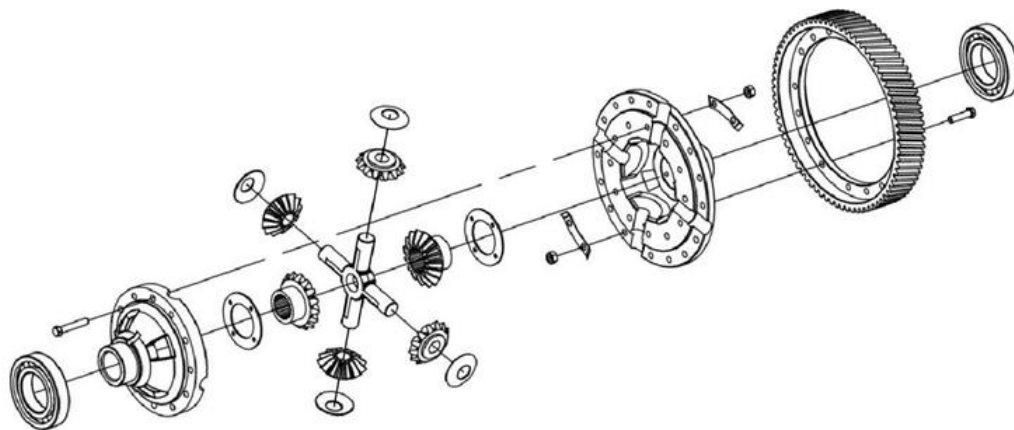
Схема конструкции дифференциала вилочного погрузчика.
